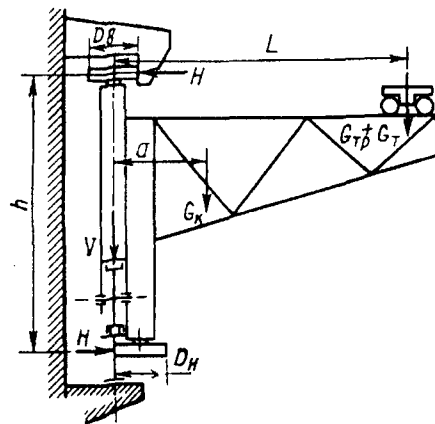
Схема определения нагрузок в опорах колес настенного консольного крана
